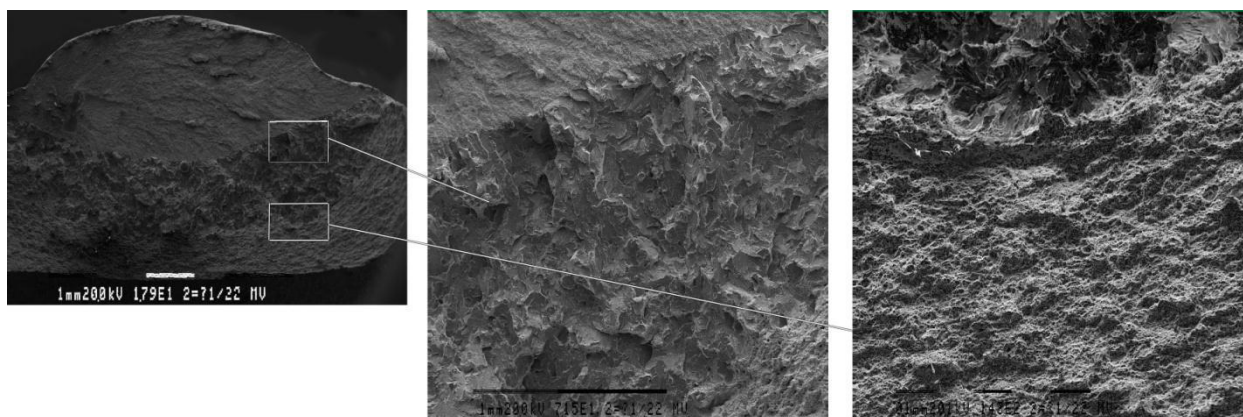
Топологія поверхні зламу зразка Э-08Х17Н8С6Г-ЦН-6Л-4,0-НД Е-300/33-2-Б40 з термічною обробкою після наплавлення
